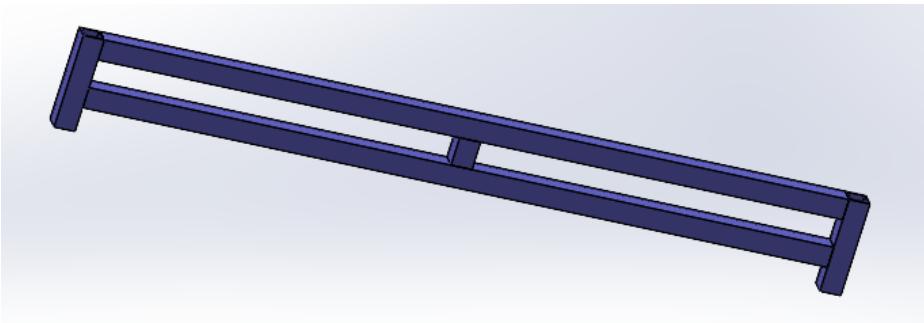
module 3D d'un assemblage du barre transversale de la base
